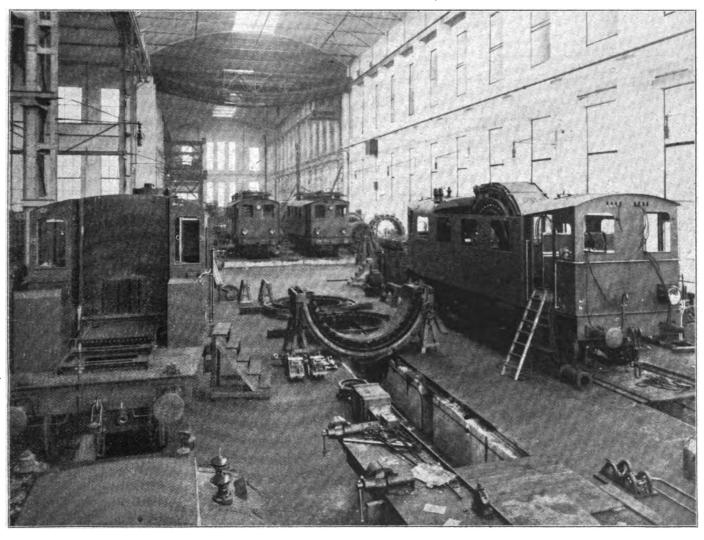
Blick in die Montagehalle der M. S. W.-Wildau. (Links 1 C 1-Schnellzuglokomotive mit Plattform für den Transformatorkessel.)
